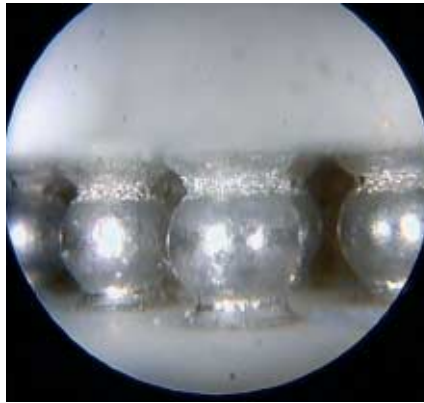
Inspektion mit starrem Endoskop, CBGA, Prozessfehler Lötstelle oben
